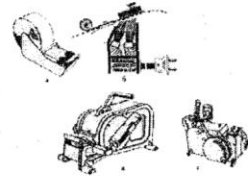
Пристрої для формування і складування коробки: а - ручне пристосування; б - заглушувальний вузол з підтримкою води; в - механізоване пристосування; г - установка з друкарським пристроєм.
